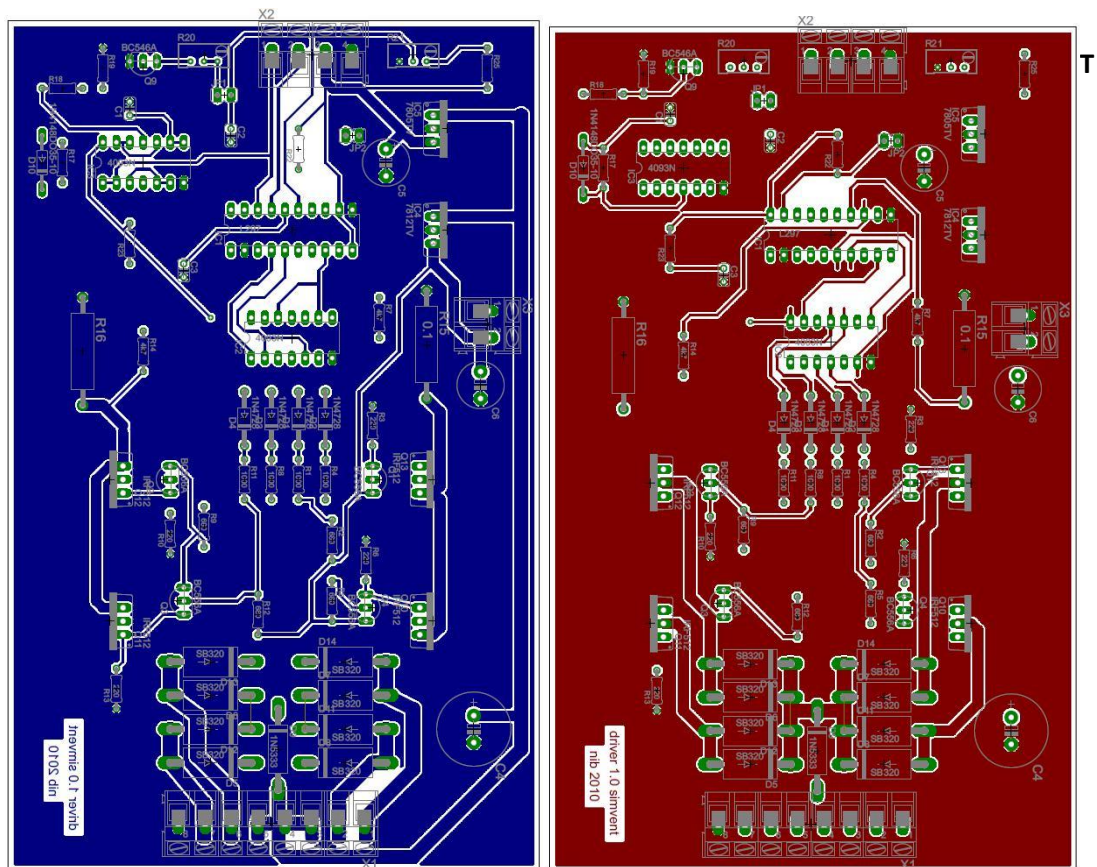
Layout controlador de motor complacencia, layout fondo azul capa inferior, layout rojo capa superior - fuente SIMVENT.
